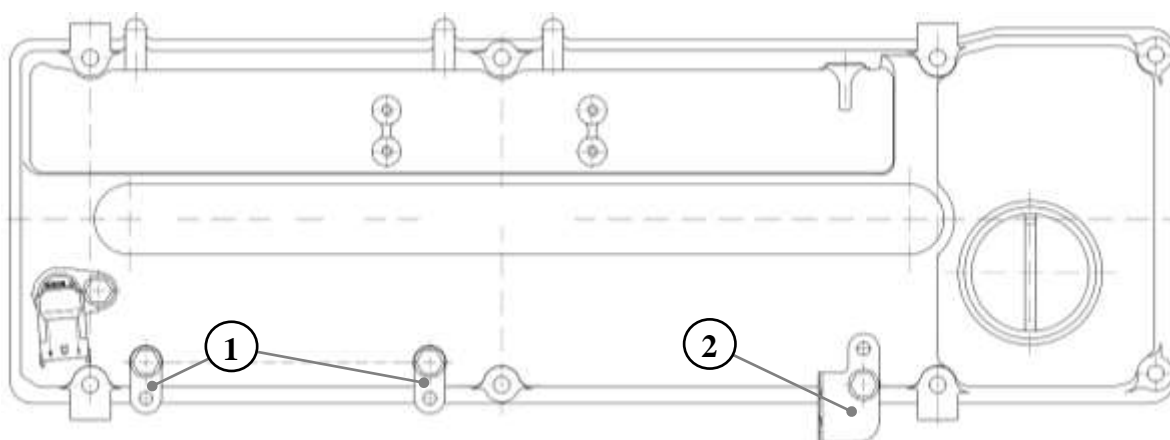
Схема установки скоб и держателей скоб крепления проводов:
